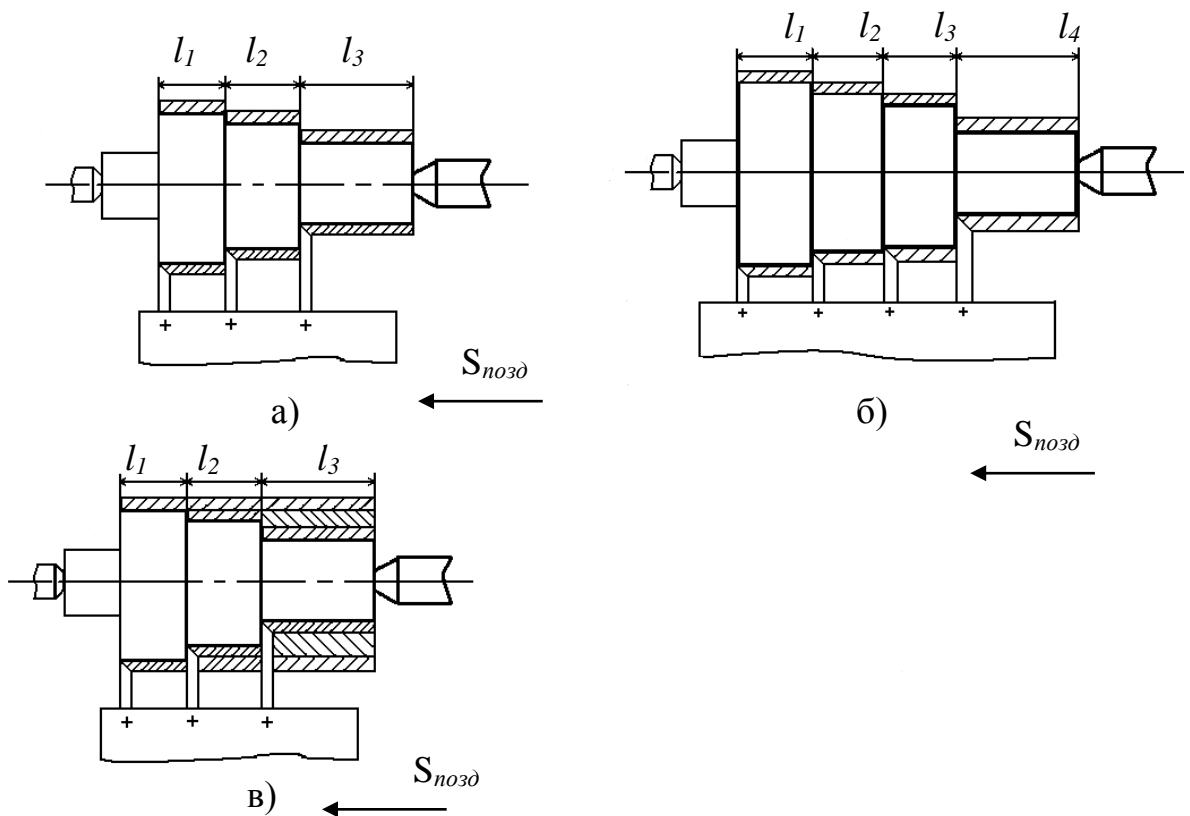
Три схеми обточування поверхонь валів на багаторізцевих верстатах
